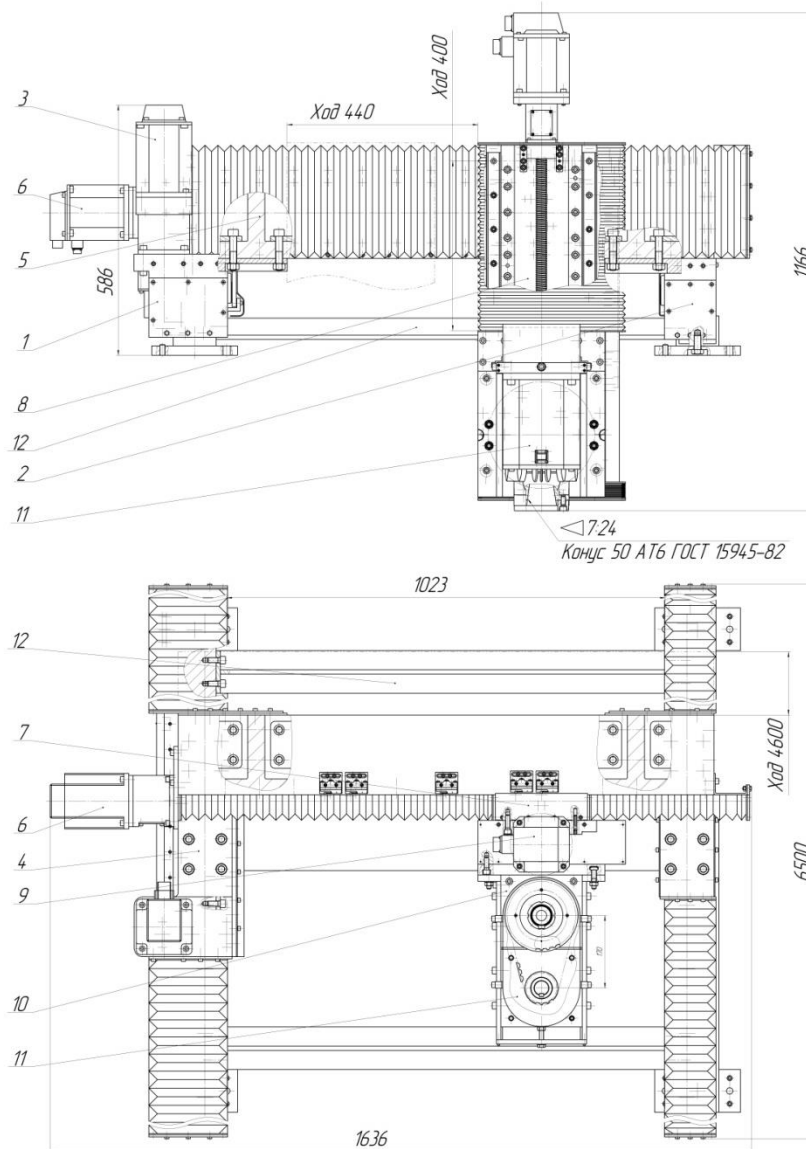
Конструктивная схема модернизируемого фрезерного станка
